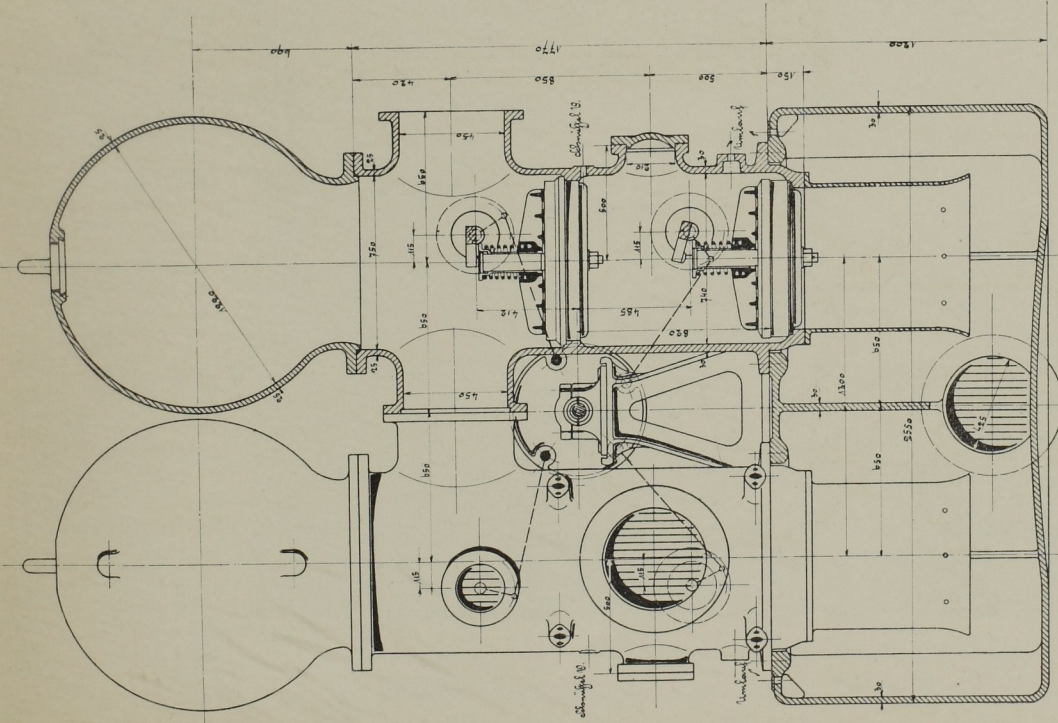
Grundriss und Schnitt der Pumpe, Masst. 1:30.
